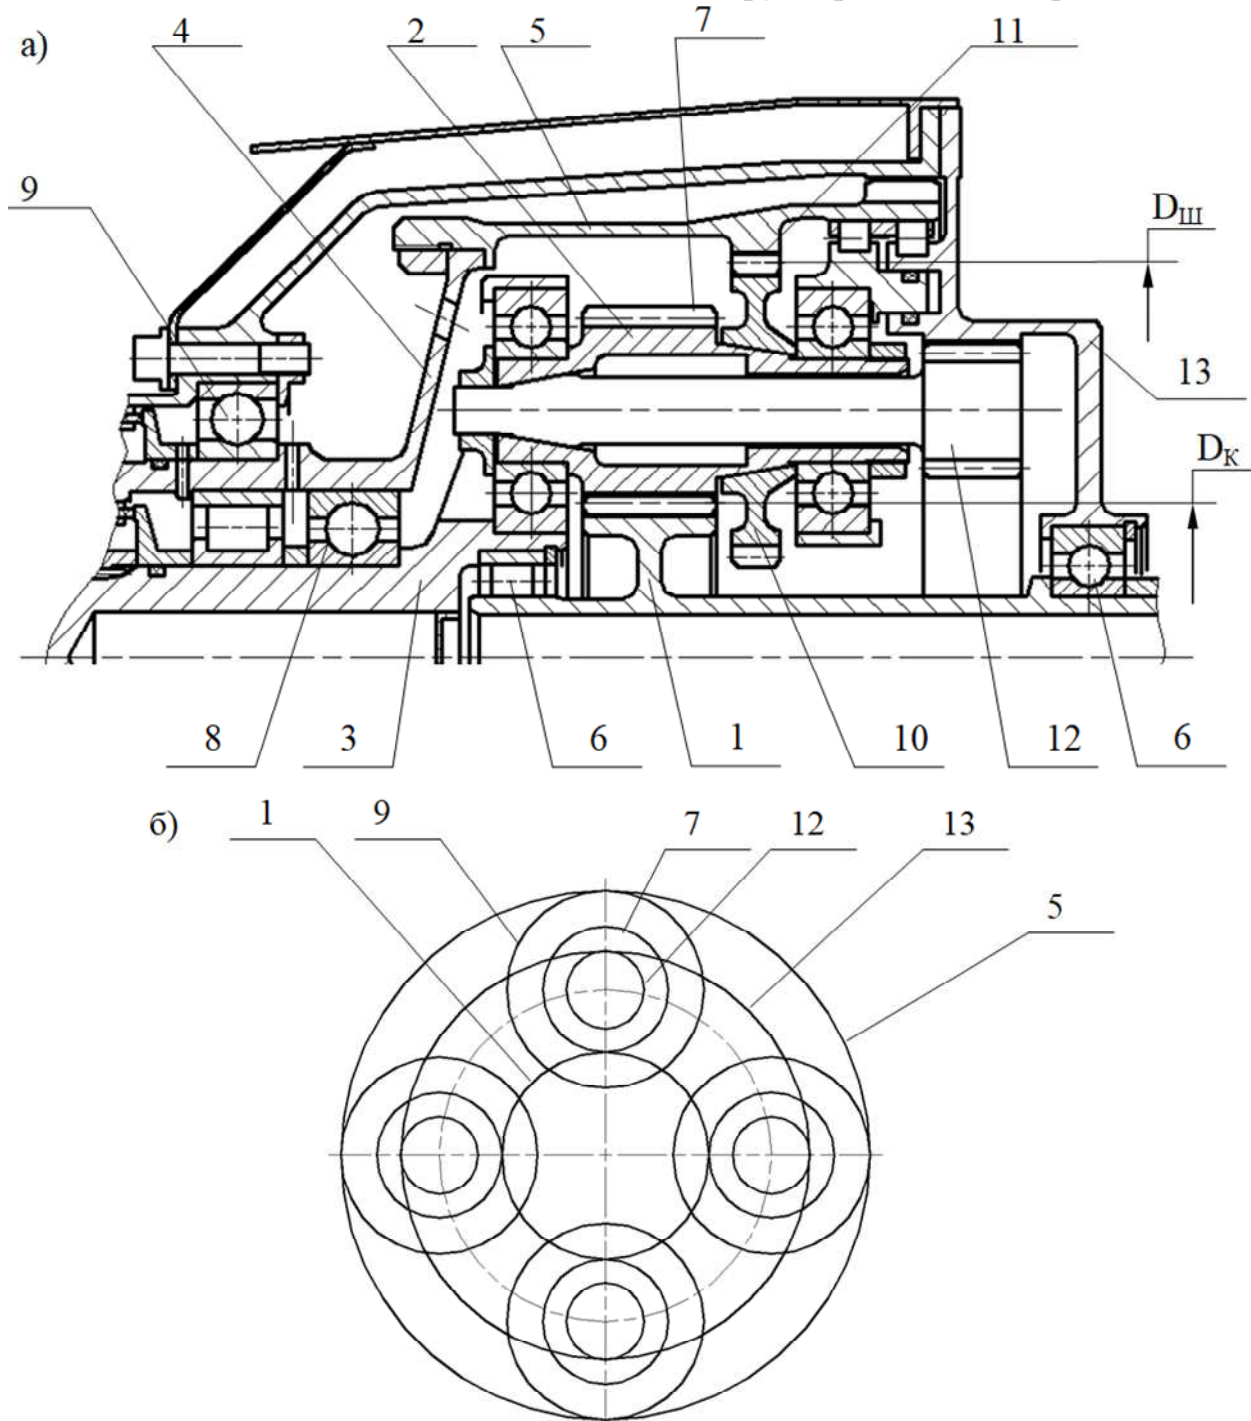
Редуктор планетарно-дифференциальный: а) продольный разрез; б) схема кинематическая
